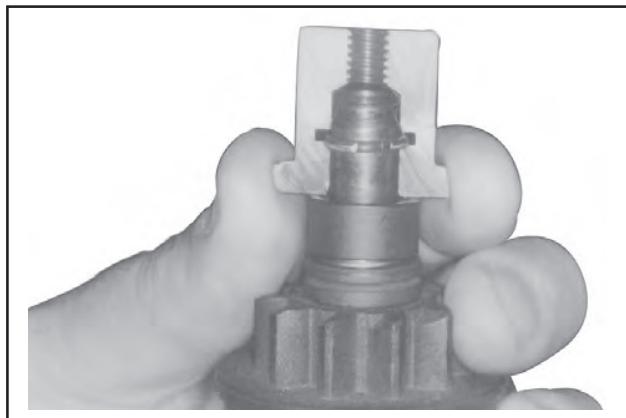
Montage der inneren Hälften des Werkzeugs um die Ankerwelle und Halterung.
